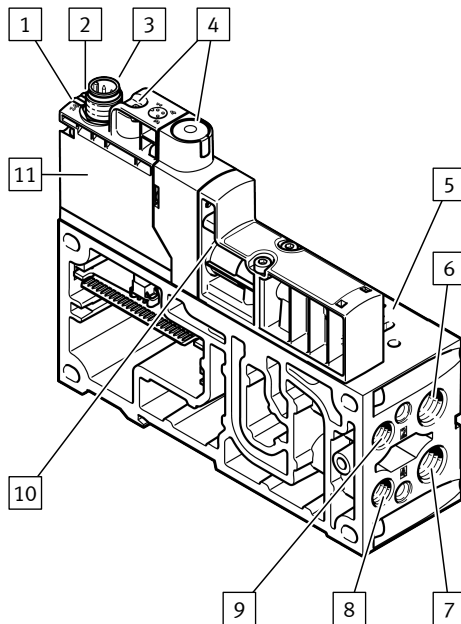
Steuerluftschaltventil mit Druckabfrage
